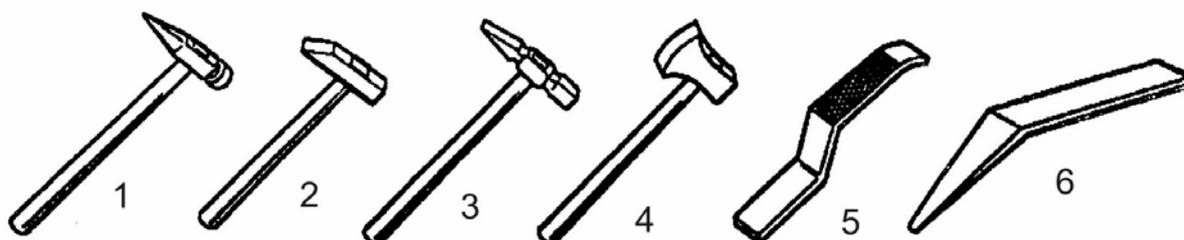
Молотки: 1 – рихтовочный; 2 – облегченного типа; 3 – для загибки фланцев; 4 – с выпуклой ударной частью; 5 – специальный с насечкой рабочей части
